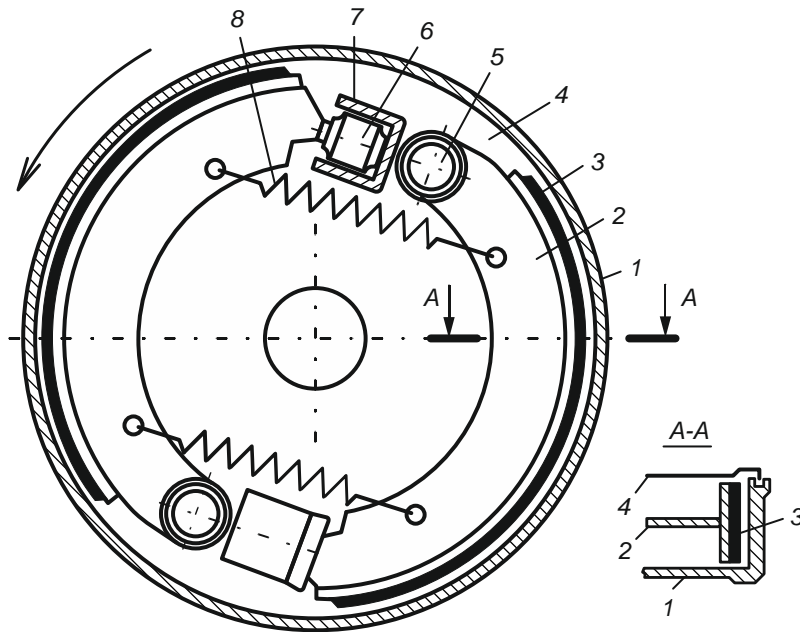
Схема колодочно-барабанного тормозного механизма переднего колеса:
